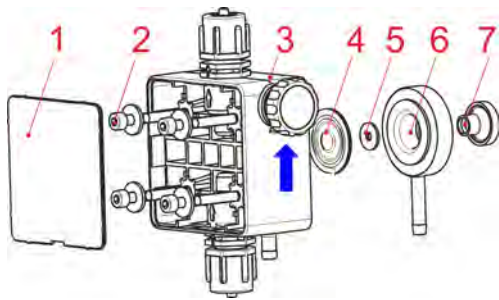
Remplacement de la membrane et de la partie supérieure de la pompe
